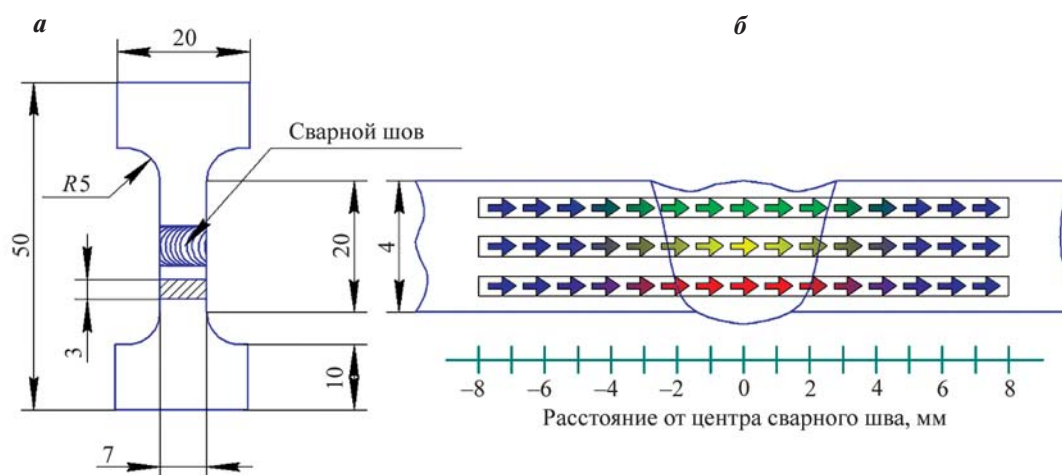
Образцы для испытаний на одноосное растяжение из пластин ВТИ-4 после плазменной сварки (а) и область измерения микротвердости в поперечном сечении сварного соединения (б)
